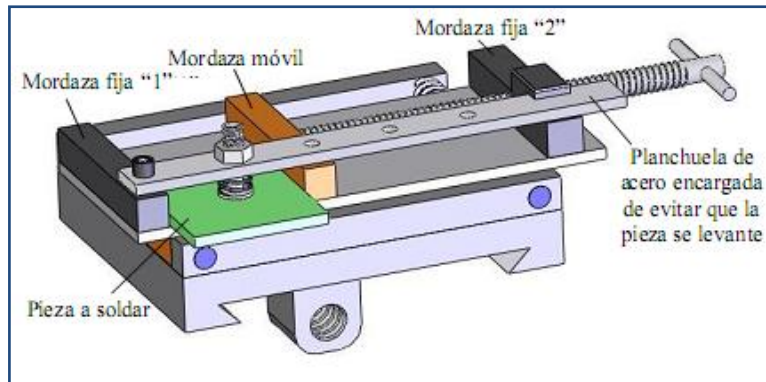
Despiece de máquina soldadora de termoplásticos.
